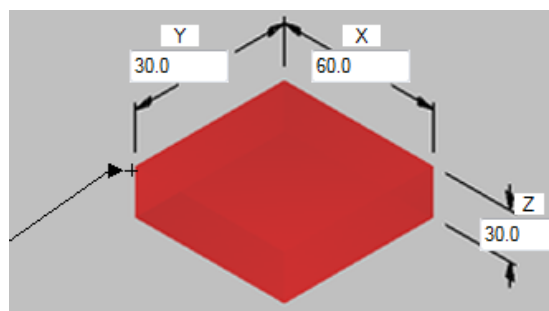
Dimensões do bloco usado na maquinagem a 3 eixos
